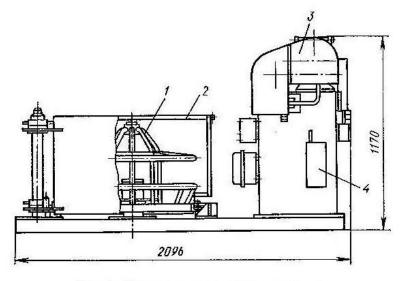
Станок для перемотки проволоки: 1— бухтодержатель, 2— защитный кожух, 3— наматыватель, 4— правидьное
